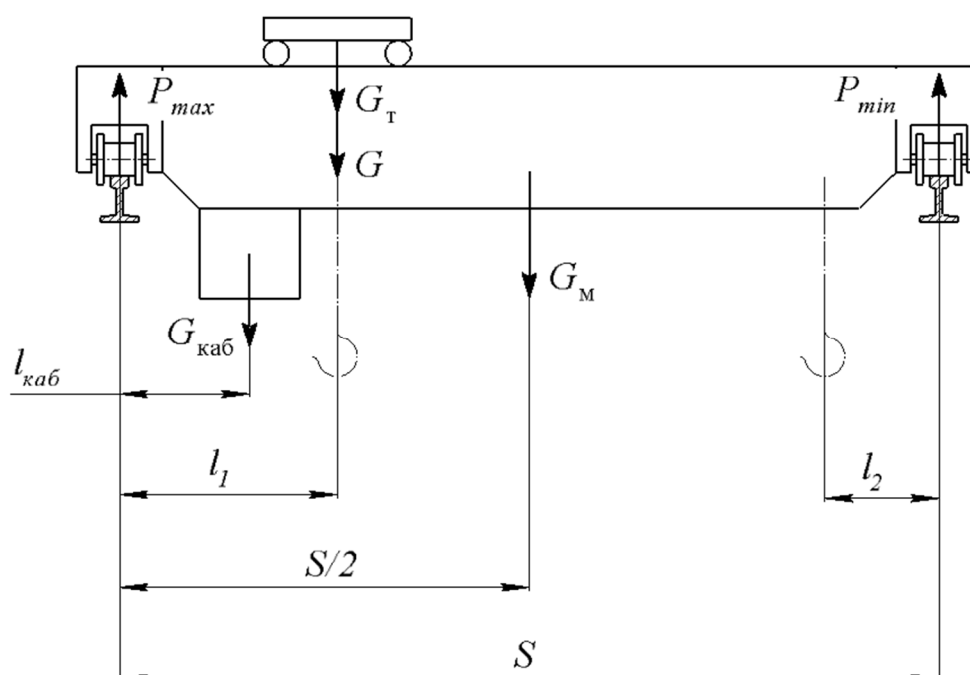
Расчетная схема для определения нагрузок на колеса крана
